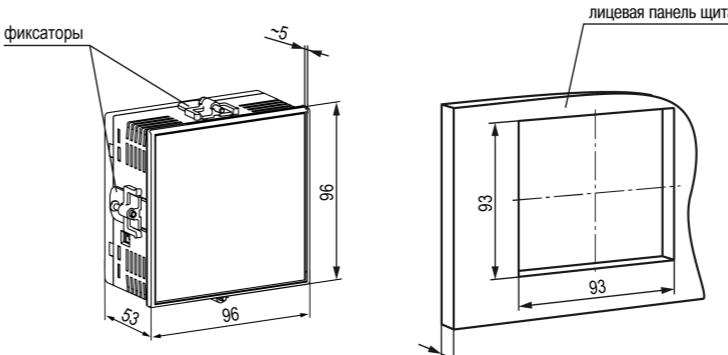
Габаритные размеры корпуса Щ1 и монтажного отверстия в щите
